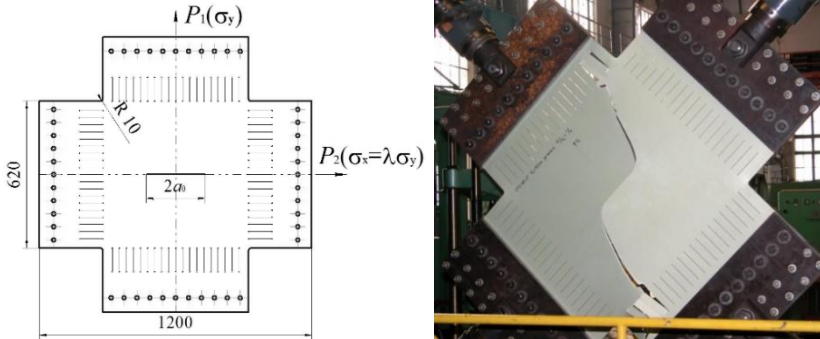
Эскиз крестообразного образца и испытанный крестообразный образец
